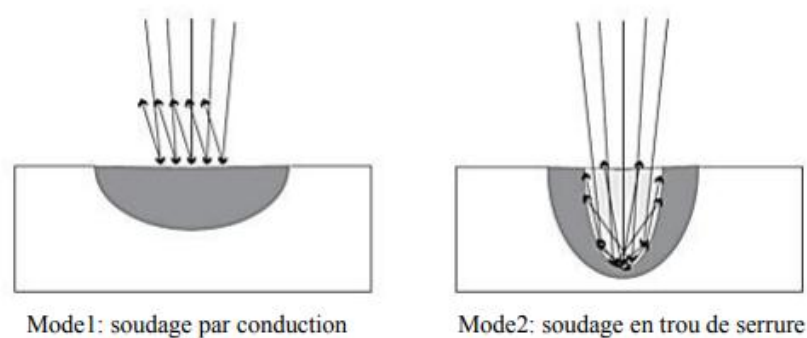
Représentation schématique du soudage laser en trou de serrure [26]
